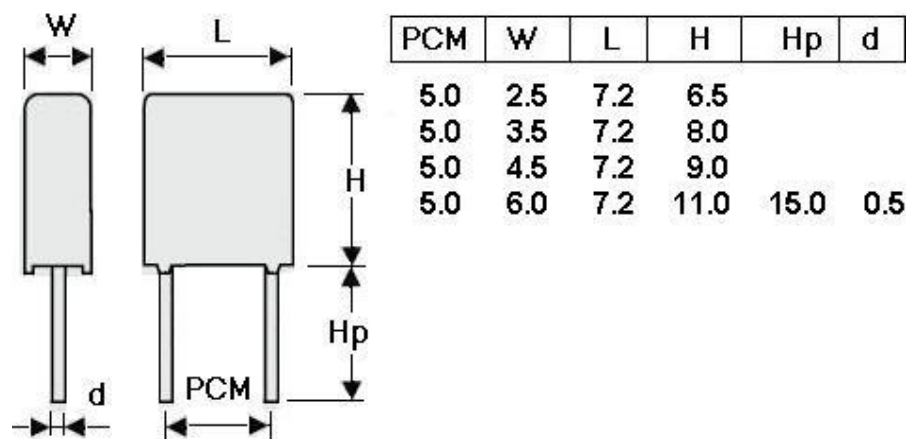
Габаритні розміри конденсатора В32529С1102J000
